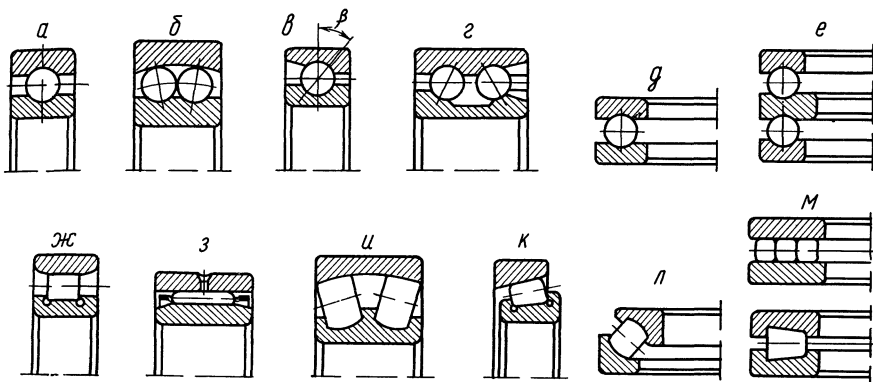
Основные типы подшипников (а, б, в, г, д, е — шарикоподшипники; ж, з, и, к, л, м — роликоподшипники)
